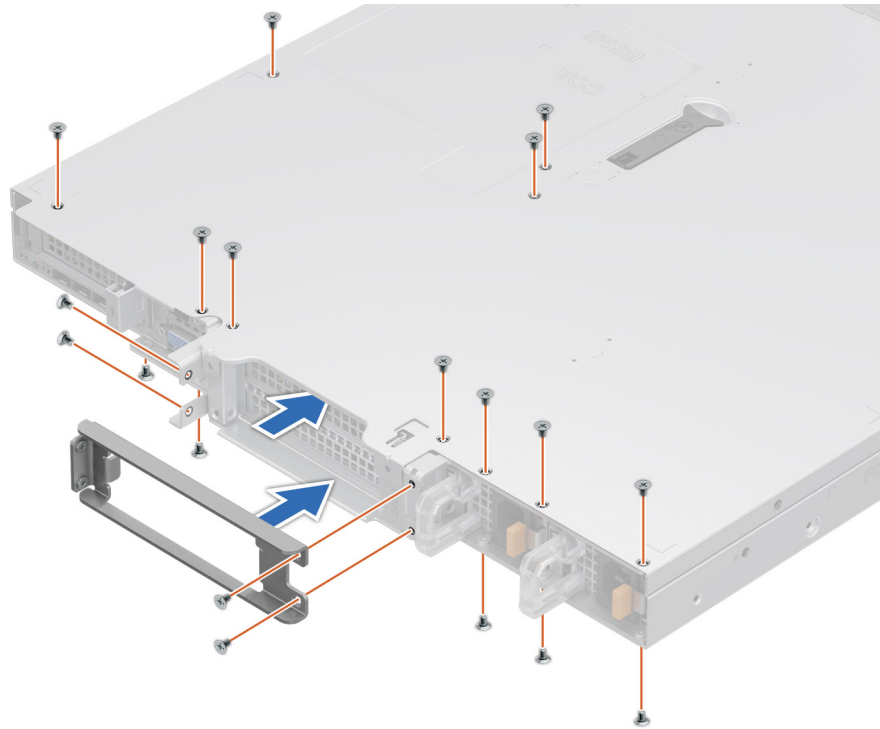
Instalación del soporte de las tarjetas elevadoras 2 y 3 y fijación de la cubierta del sistema
